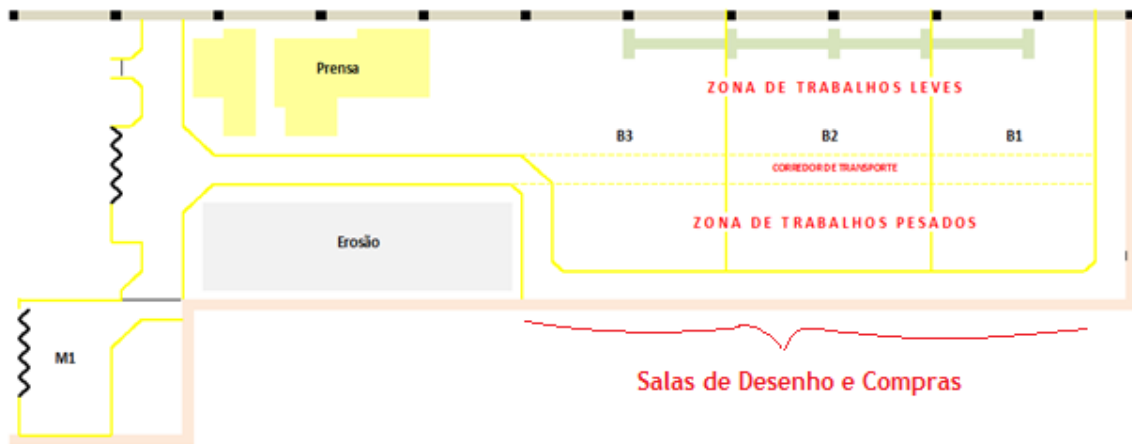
Planta preliminar da IMA: definição de zonas de trabalho e corredor.
